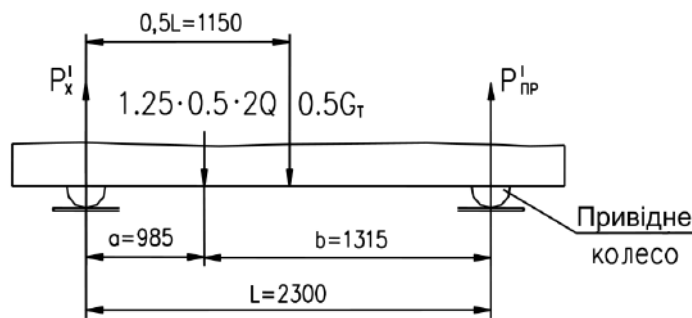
Схема навантажень на кінцеву балку візка при пересуванні з вантажем.
